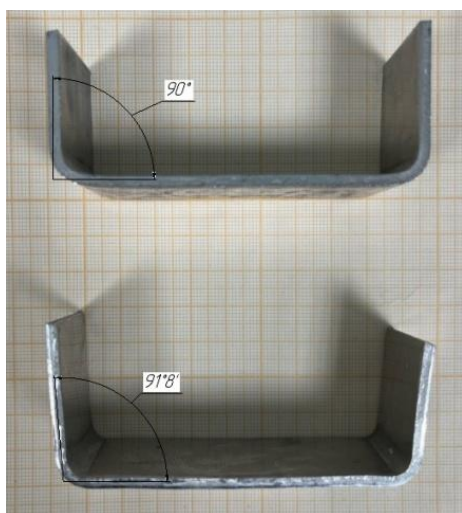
Детали из алюминиевого сплава 8011А, согнутые в штампе с (сверху) и без (снизу) упругих планок
